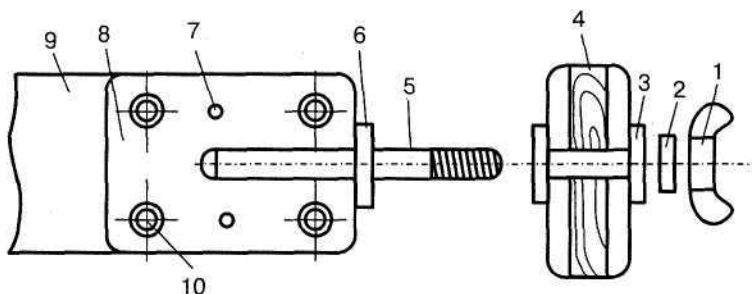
Поперечина для установки шверцов: 1 — гайка-барашек; 2, 6 — шайбы; 3 — шайба-накладка (приклеить эпоксидным клеем); 4 — шверц; 5 — шпилька с резьбой М12; 7 — отверстия под болты крепления поперечины к корпусу; 8 — стальная пластина (3x90x125 мм); 9 — поперечина (дуб или бук 20x90 мм); 10 — болт М6 с гайкой
